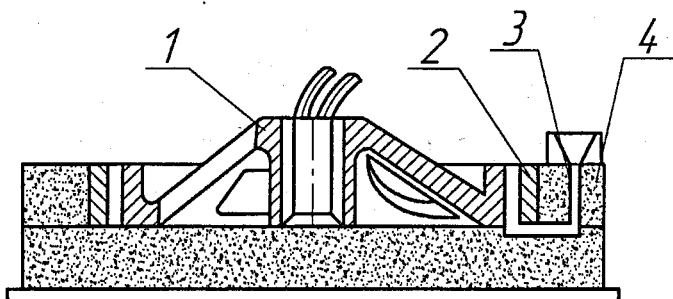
Відновлення зношеного шару деталі заливанням рідким металом: 1 – опорний коток; 2 – кокіль; 3 – ливникова система; 4 – опока
